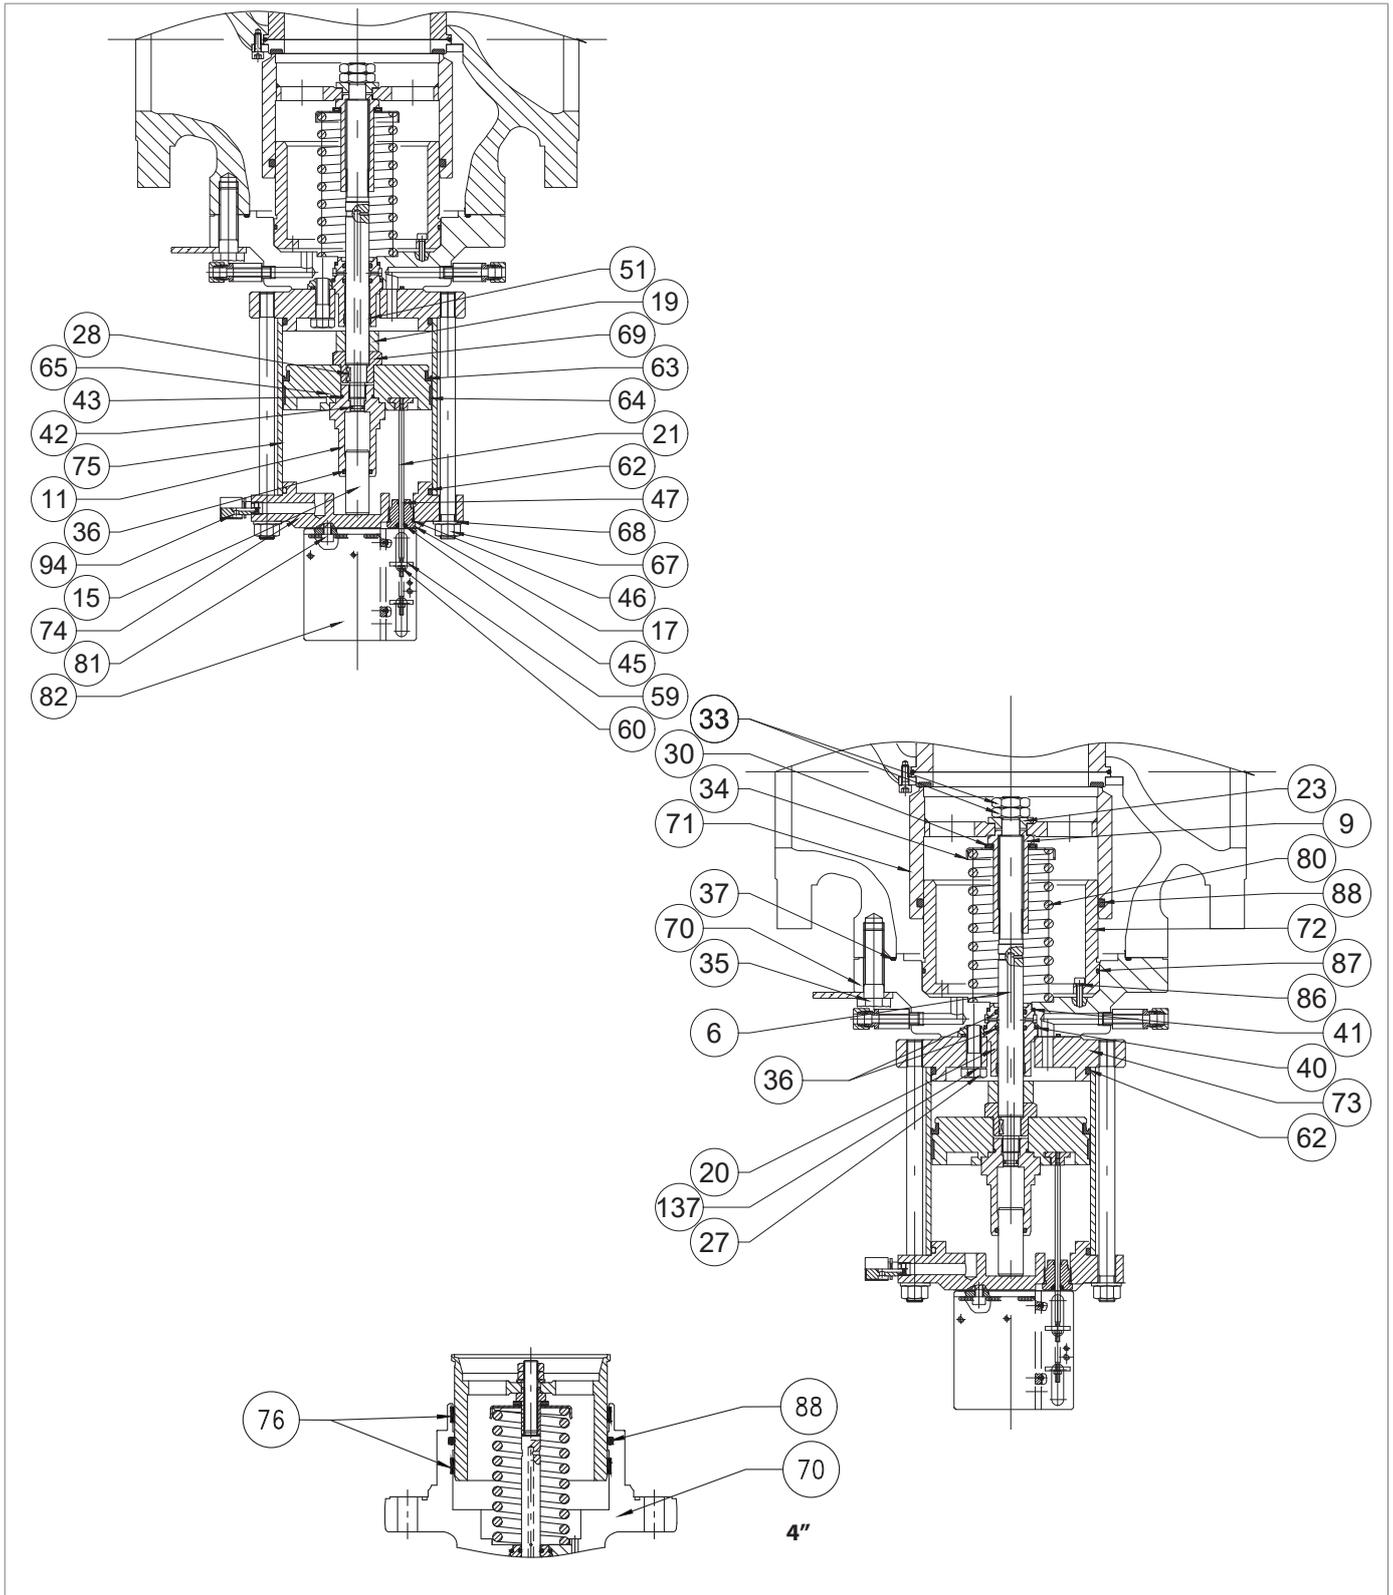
Встроенный предохранительный запорный клапан НВ/97
